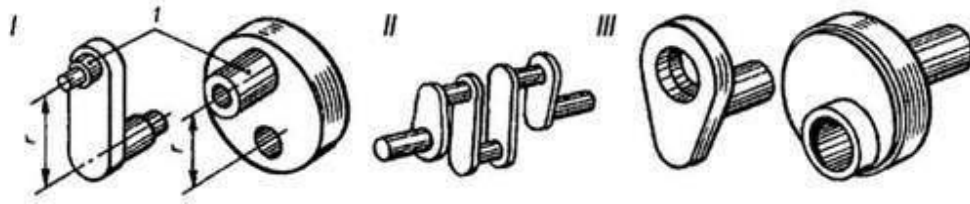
Кривошипный механизм — механизм, преобразующий один вид движения в другой
